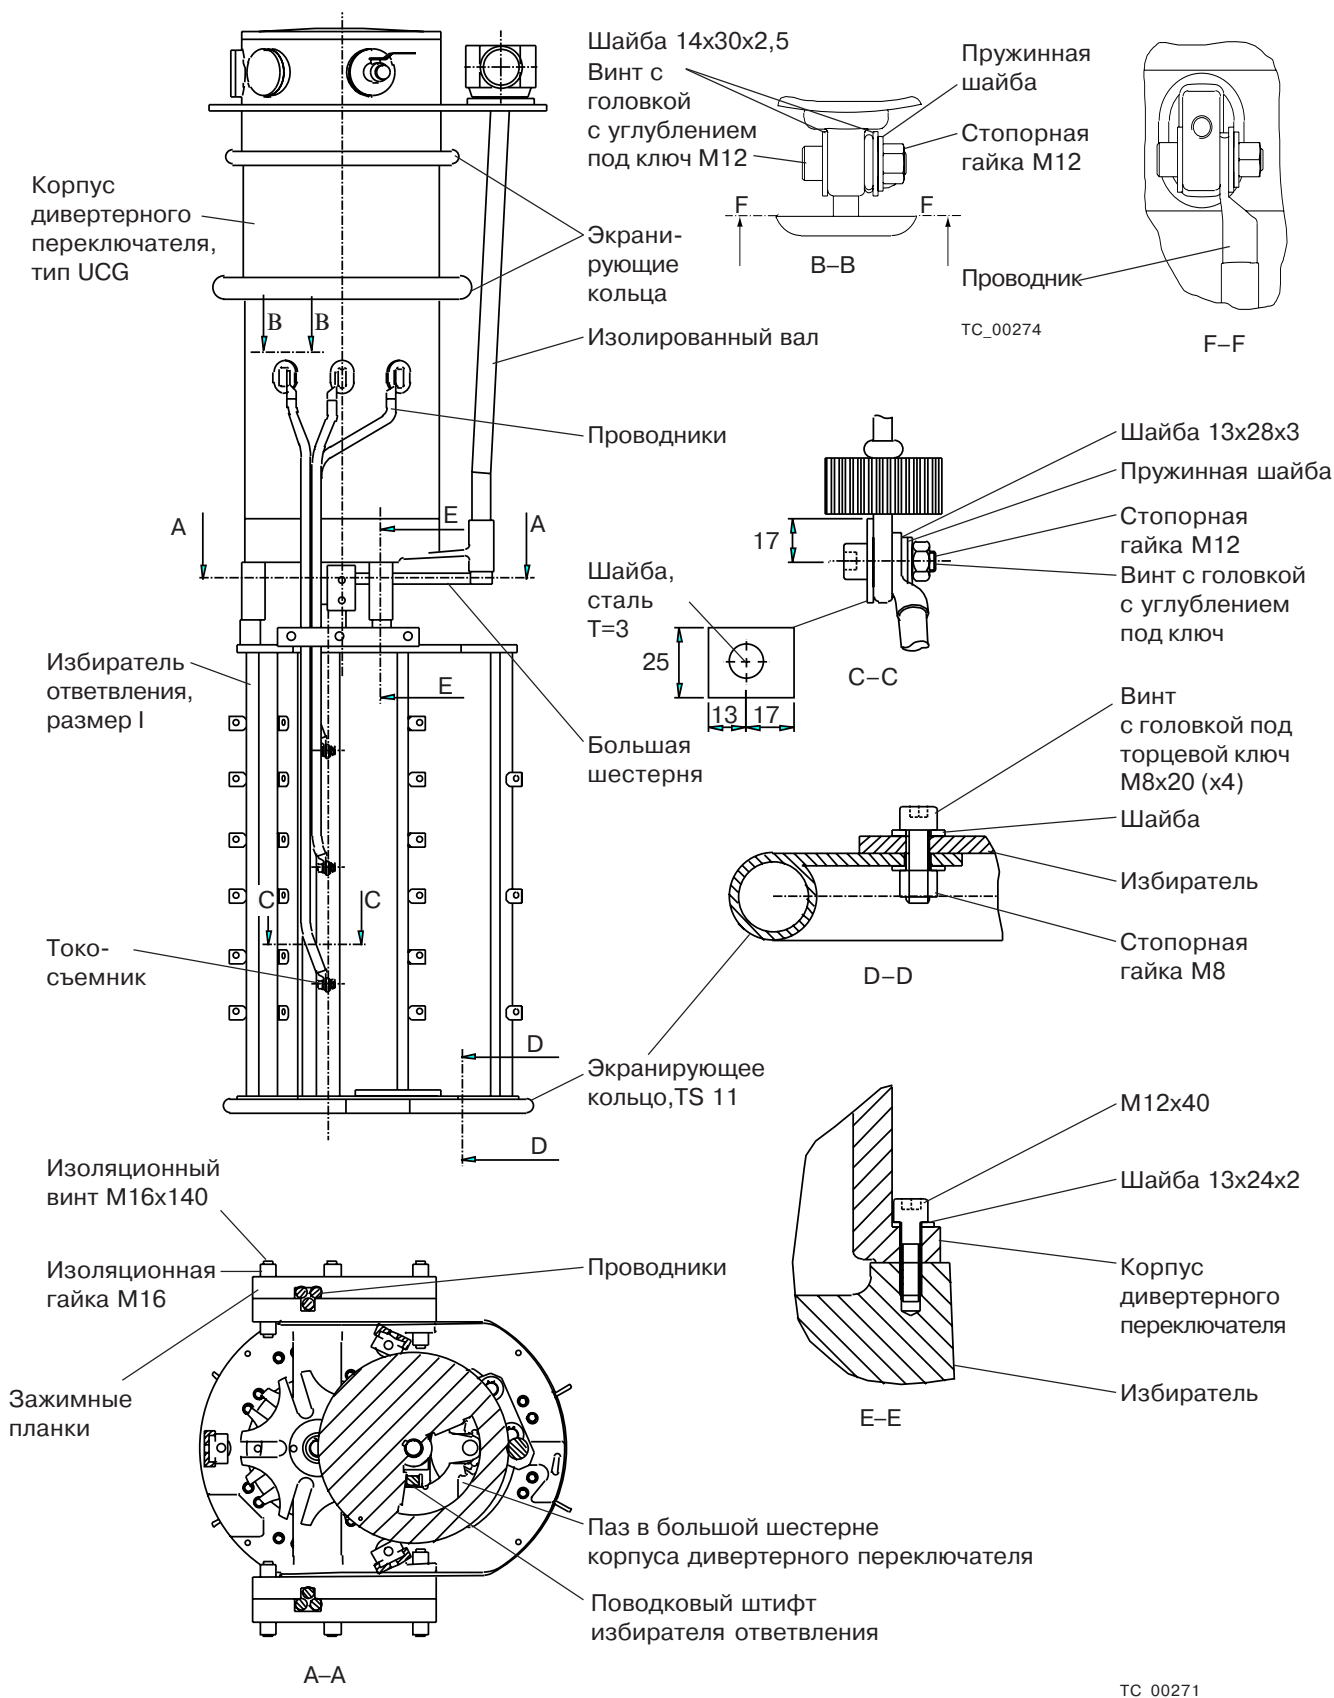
Избиратель отвлечения, размер I, и дивертерный переключатель типа UCG
